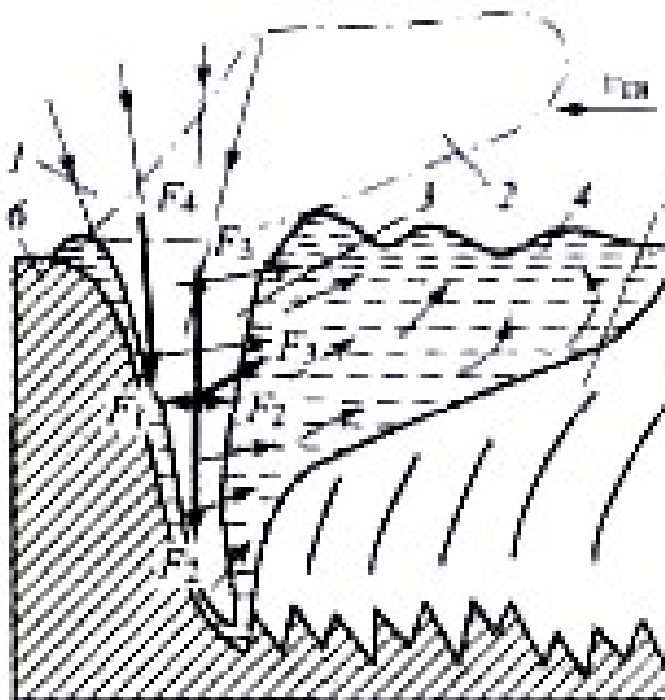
Схема продольного сечения сварочной ванны
